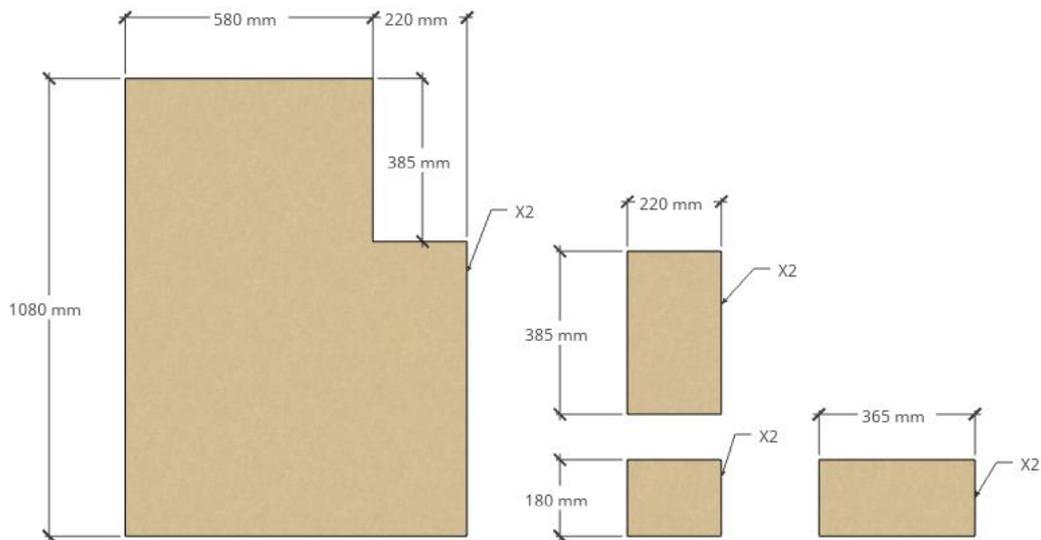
Despiece módulo garaje. Fuente: Elaboración propia
